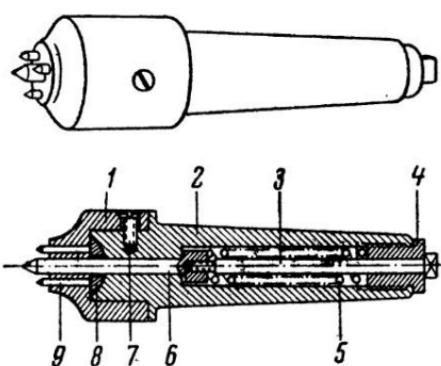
Поводковый передний центр со шпильками: 1 — головка; 2 — корпус; 3 — винт; 4 — гайка; 5 — пружина; 6 — центр; 7 — стопорный винт (3 штуки); 8 — шайба опорная; 9 — поводок (3 штуки).
